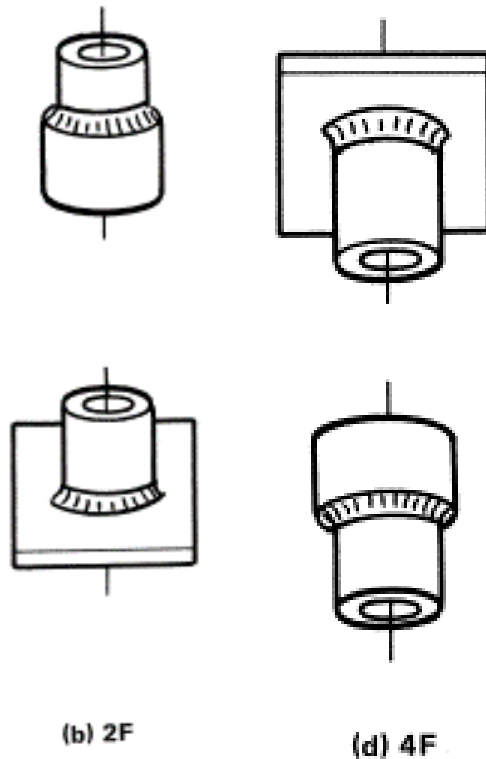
Soldadura de filete en unión entre tuberías y tubería-lámina.
